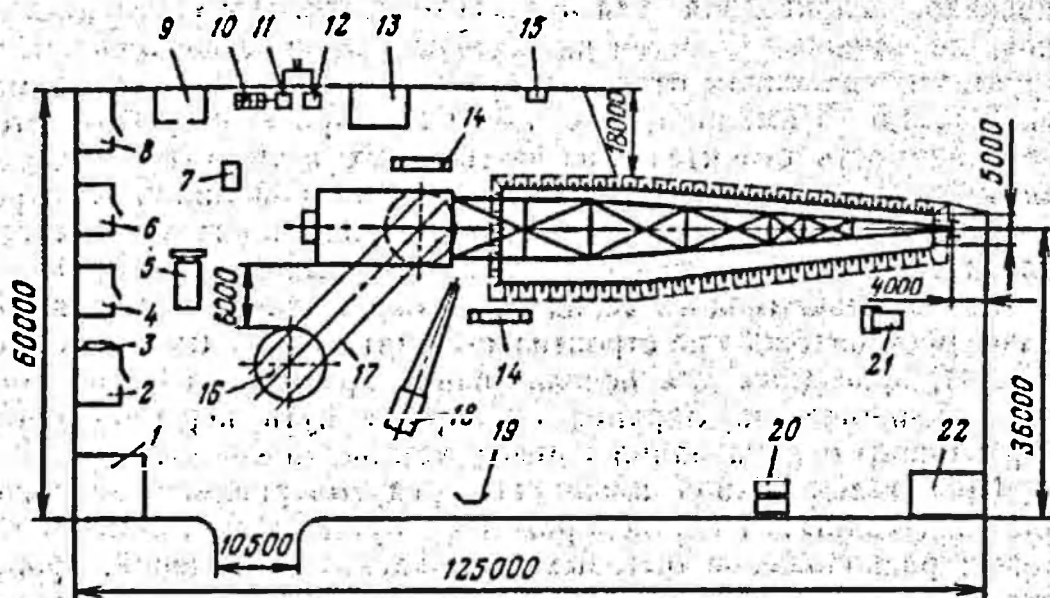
Схема монтажной площадки шагающего экскаватора:
